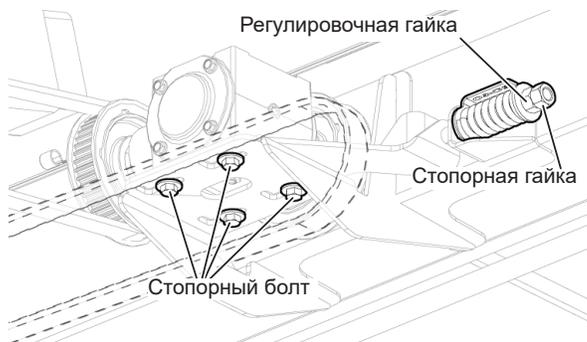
Регулировка натяжения второго ремня правого полотенного транспортера
